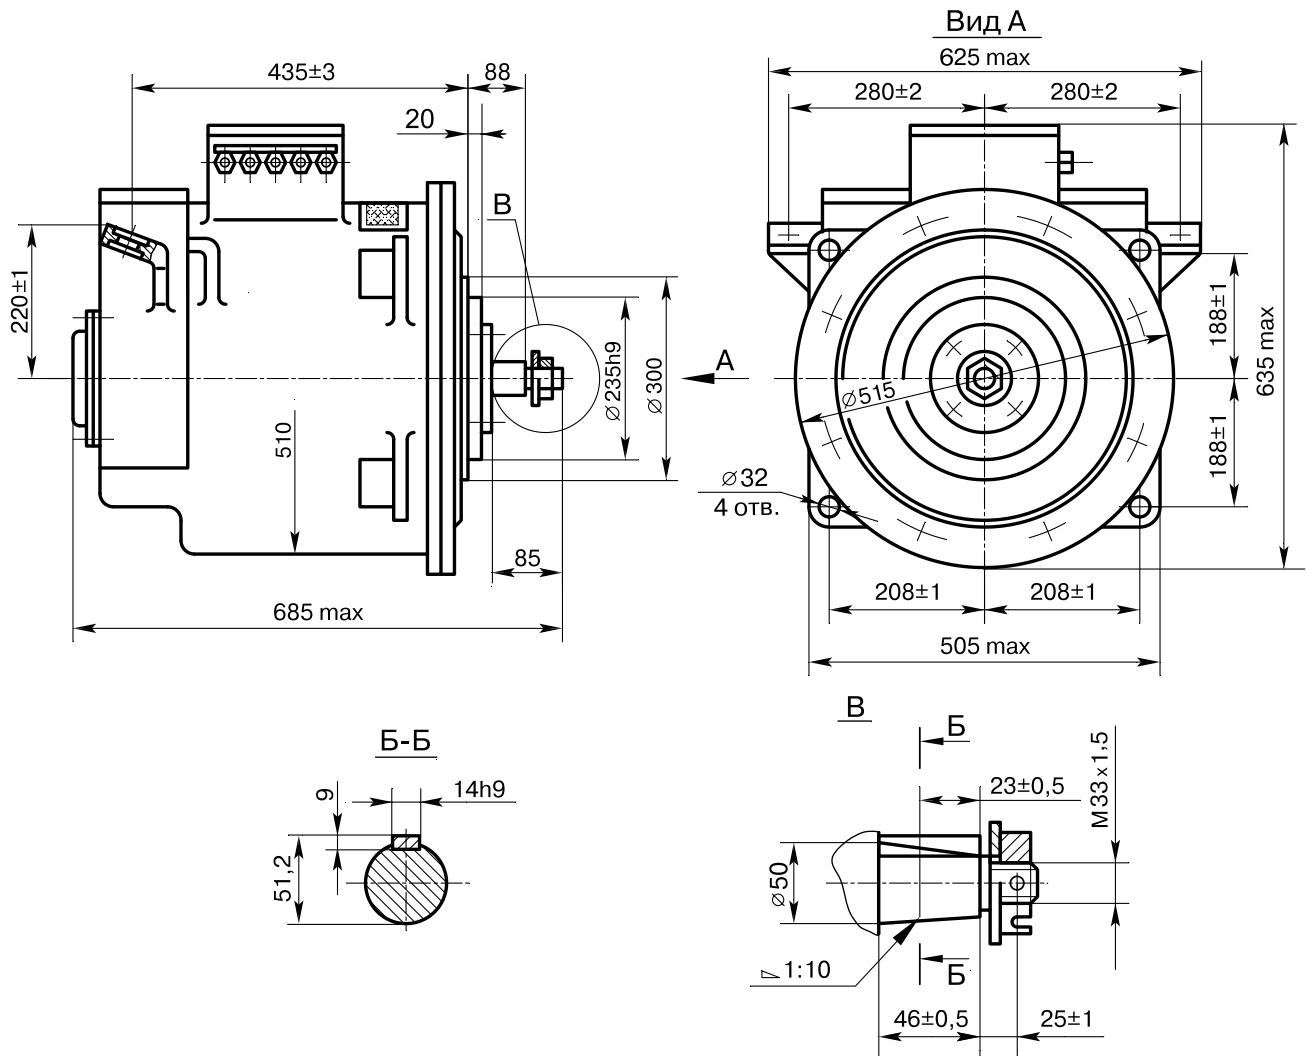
Габаритные и установочные размеры электродвигателя ДТН–33/20
